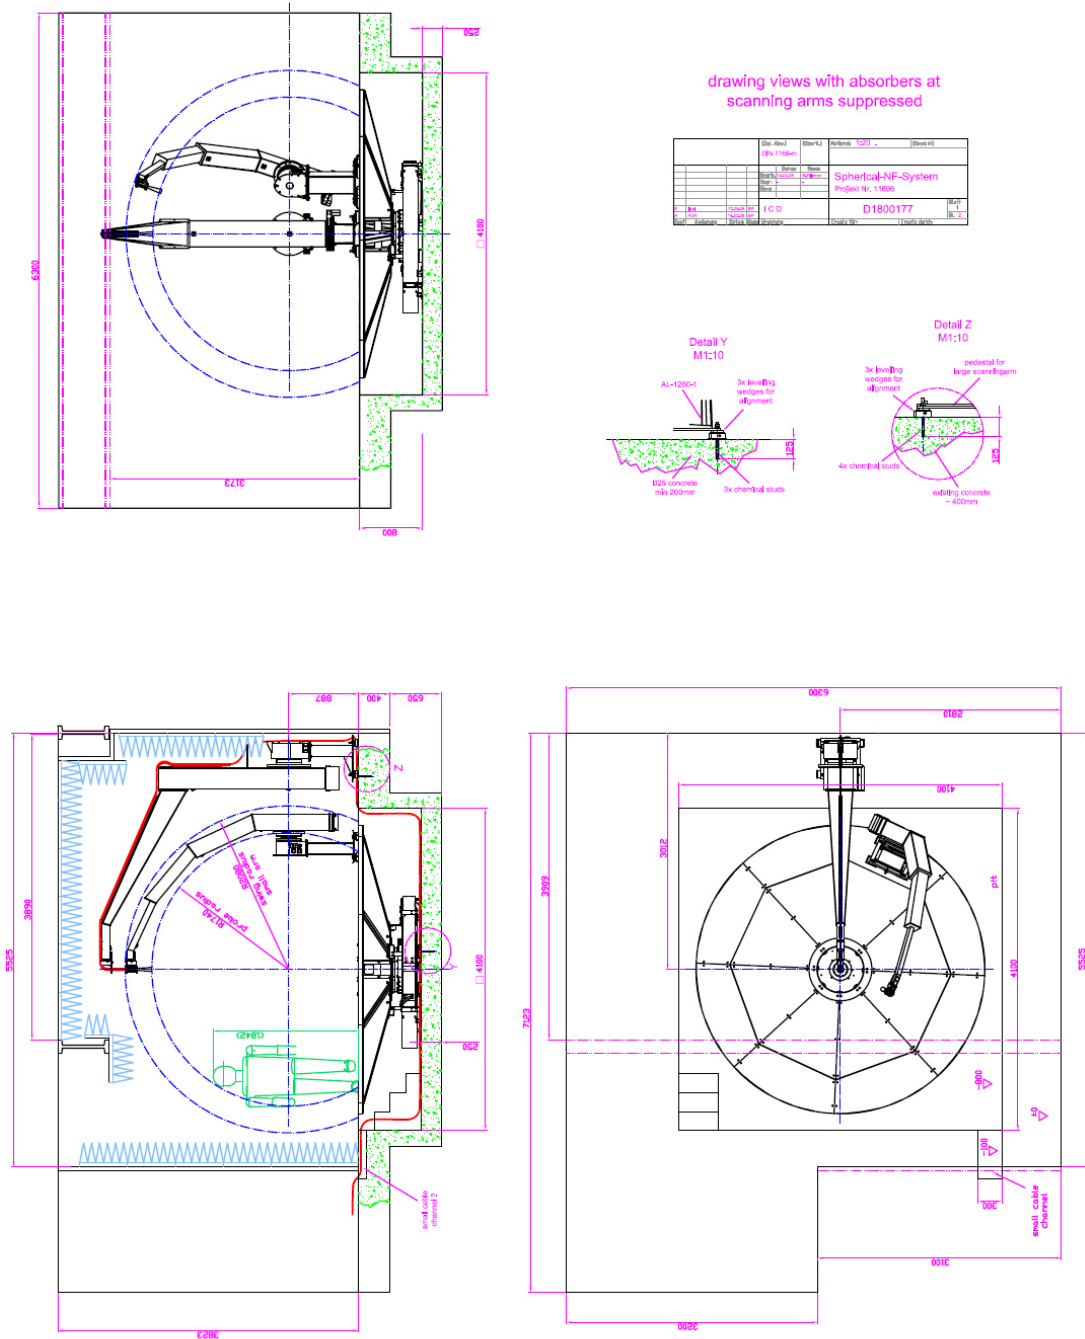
Plano definitivo en planta y alzado del diseño final
